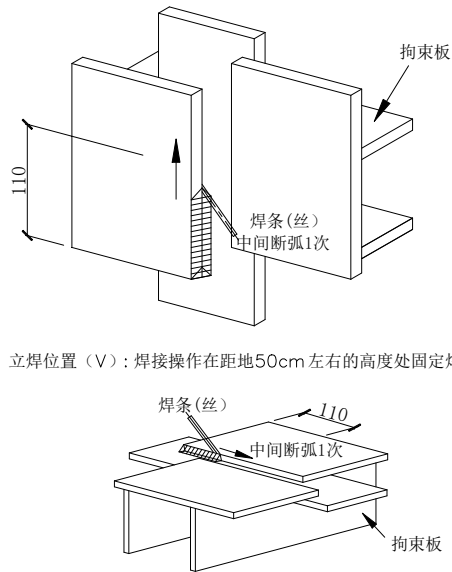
2-1 搭接角焊缝试件形式、尺寸和试样取样位置示意
